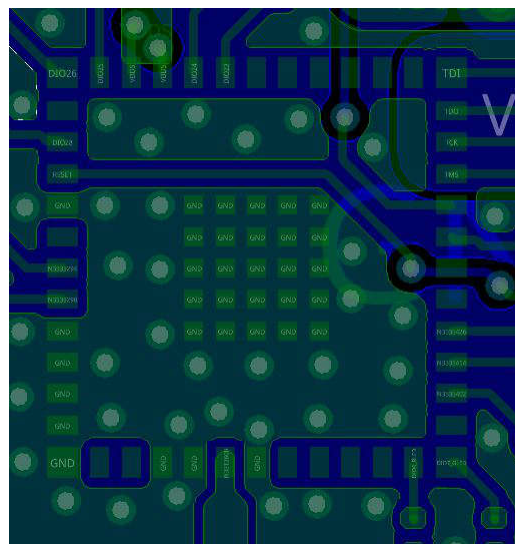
CC1312PSIP 正下方 2 层 PCB 的顶层和底层
